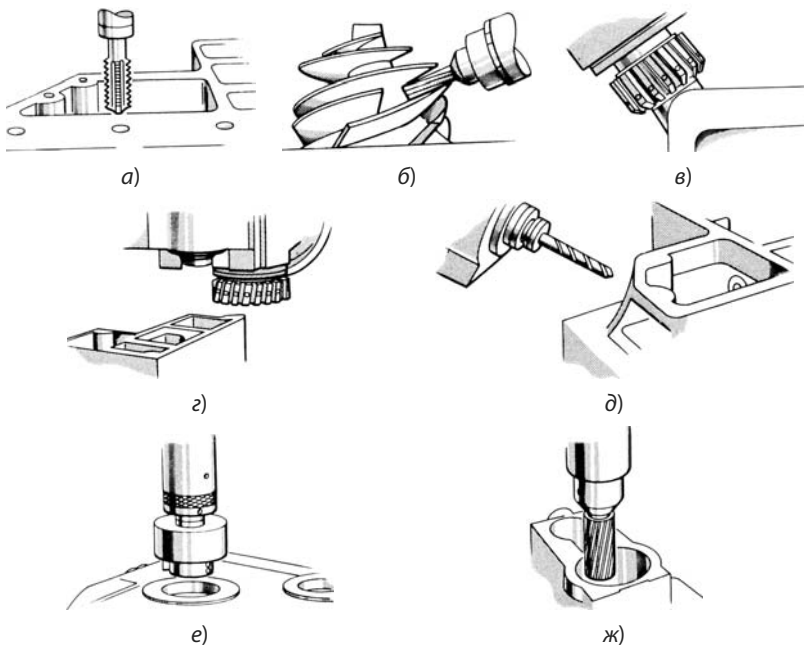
Технологические переходы, выполняемые на многоцелевом станке: а — нарезание резьбы; б — контурное объемное фрезерование; в — фрезерование поверхности, расположенной под любым углом; г — фрезерование торцевой фрезой горизонтальной поверхности; д — сверление под любым углом; е — расточка; ж — фрезерование концевой фрезой
